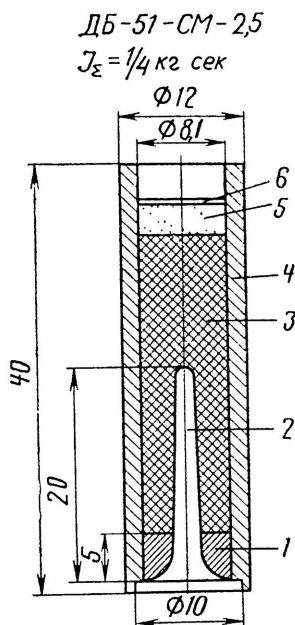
Модельный ракетный двигатель ДБ-51-СМ-2,5:
